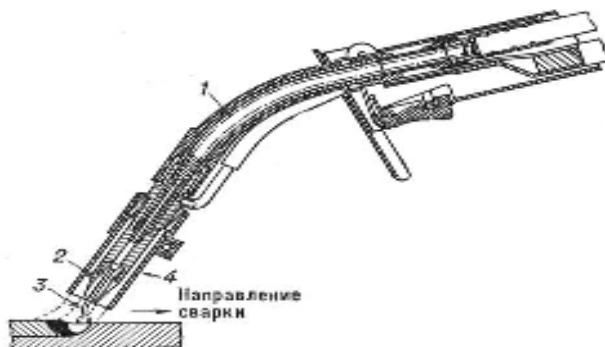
Устройство сварочной горелки с подачей защитного газа
